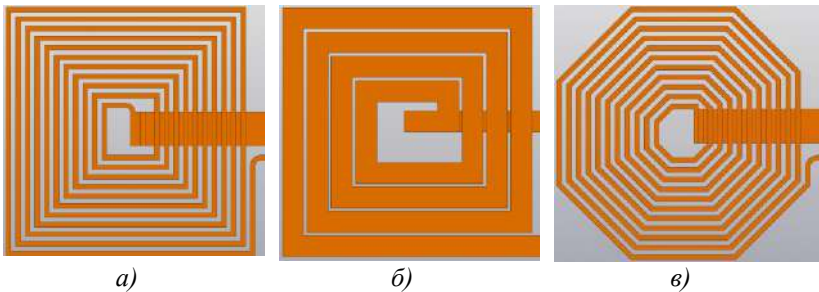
Индукторы разной формы: а) квадратный, выполненный из пластин, перпендикулярных заготовке; б) квадратный из пластин, параллельных заготовке; в) октагональный из пластин, перпендикулярных заготовке
